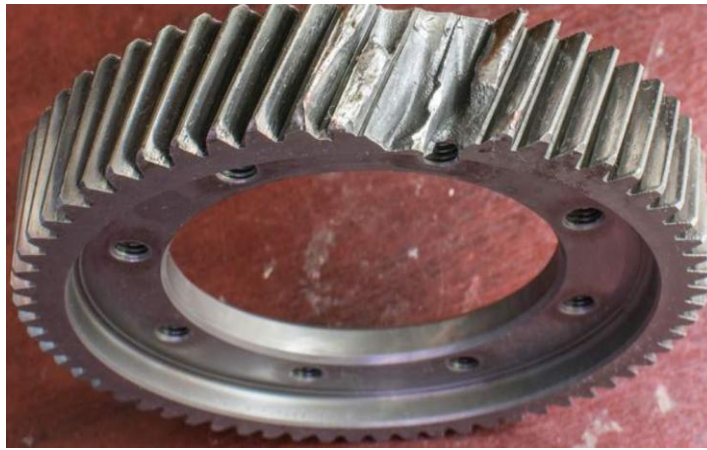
Зовнішній дефект шестерні коробки передач, виявлений за допомогою візуального контролю
